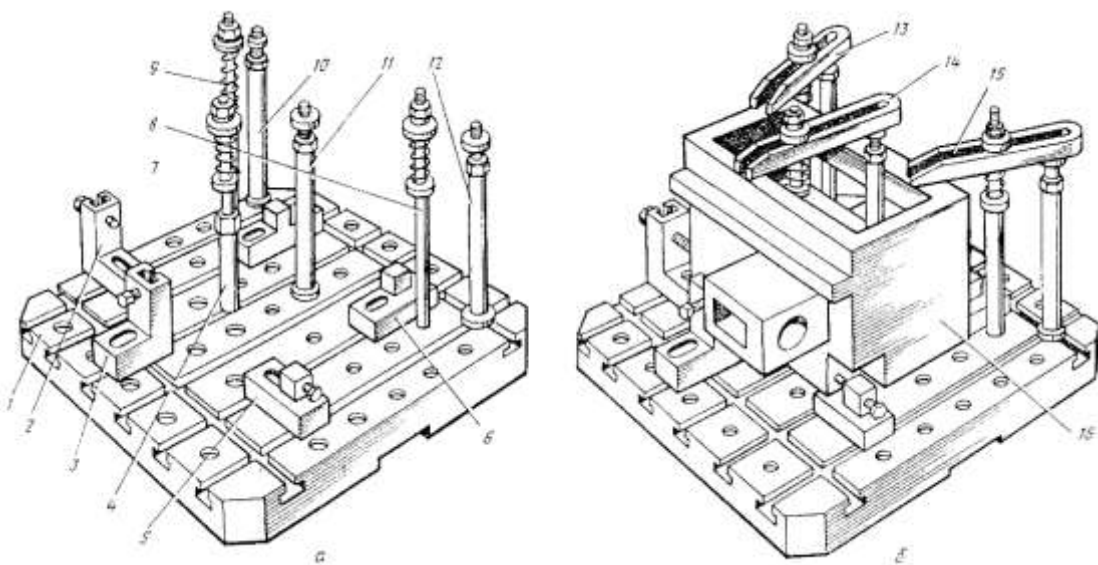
Закріплення заготовки на палеті: а – плита з базовими кріпильними елементами;
